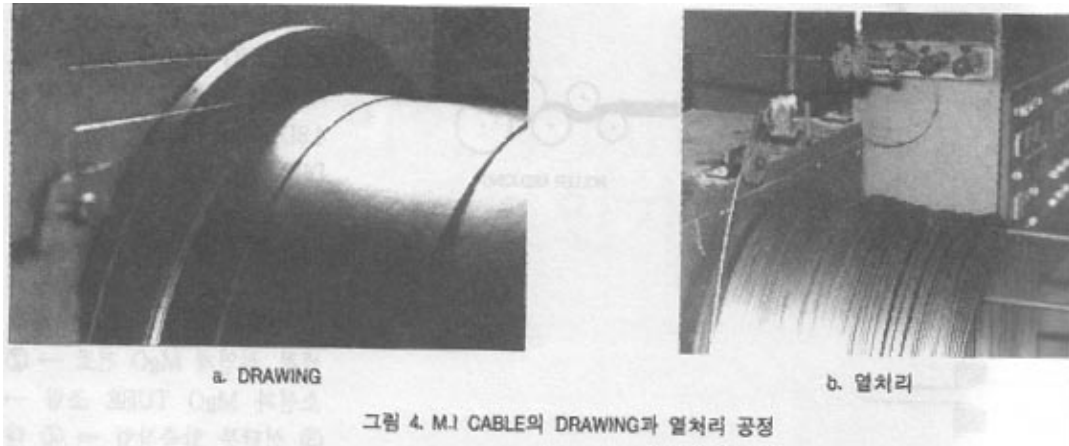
M.I. CABLE의 DRAWING과 열처리 공정
